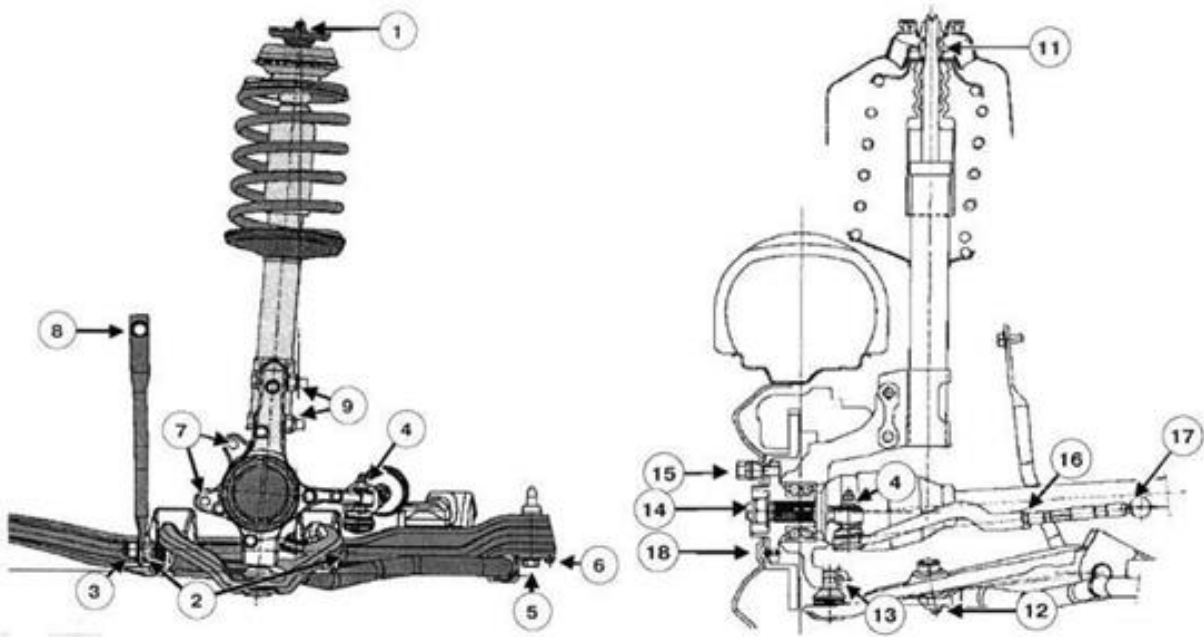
Моменти затяжки різьбових з'єднань елементів передньої підвіски
